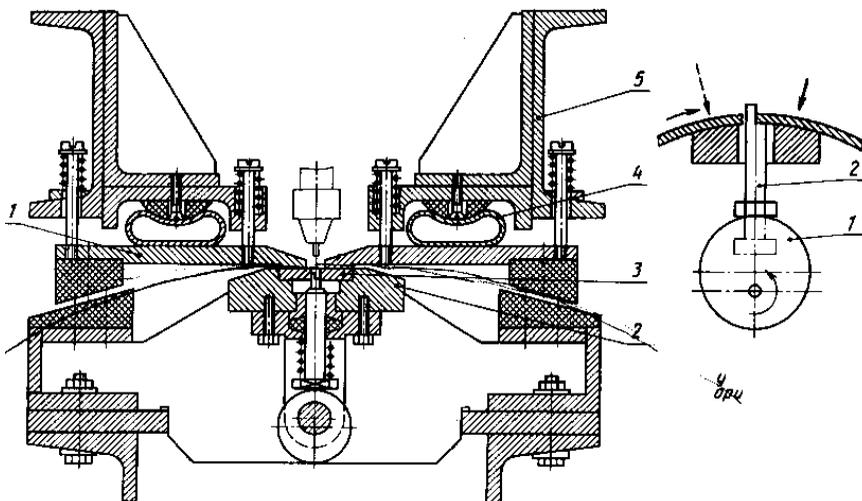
Приспособление для сборки и сварки стыковых прямолинейных швов
